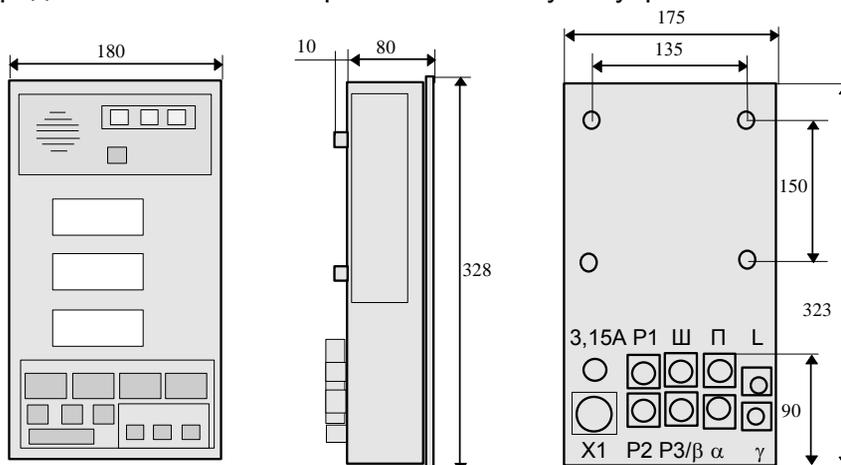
Габаритные и присоединительные размеры БОДа
